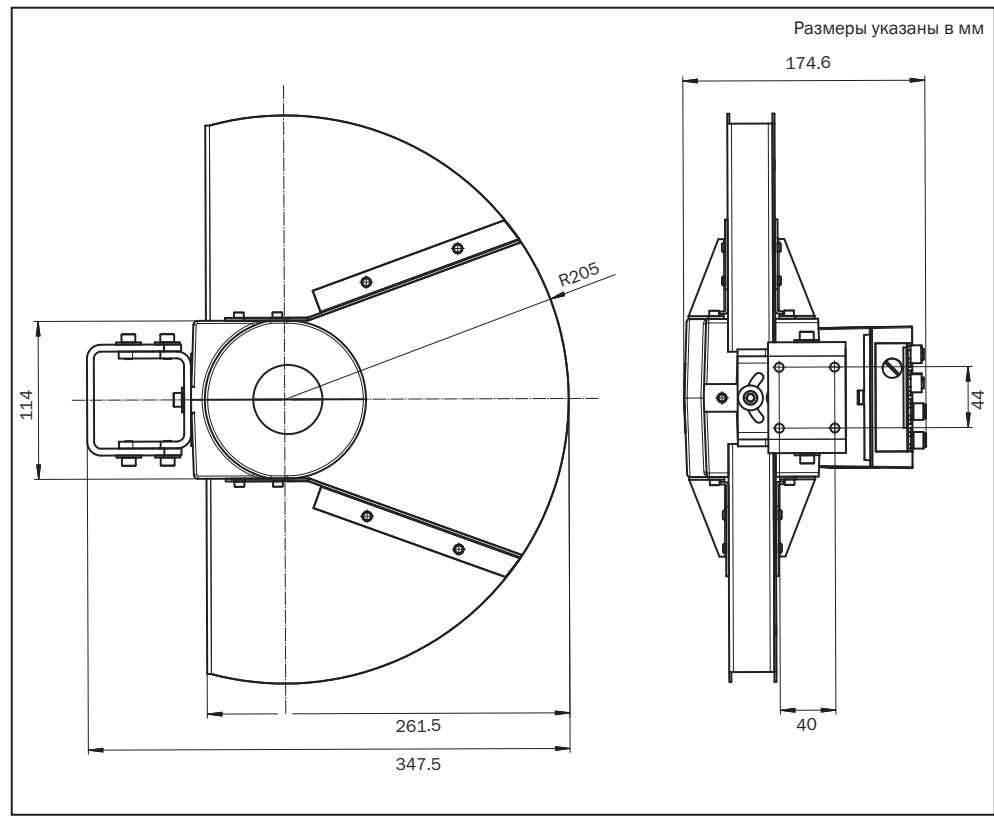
Размерный чертеж погодозащитного кожуха 190° (Артикул 2046459)
